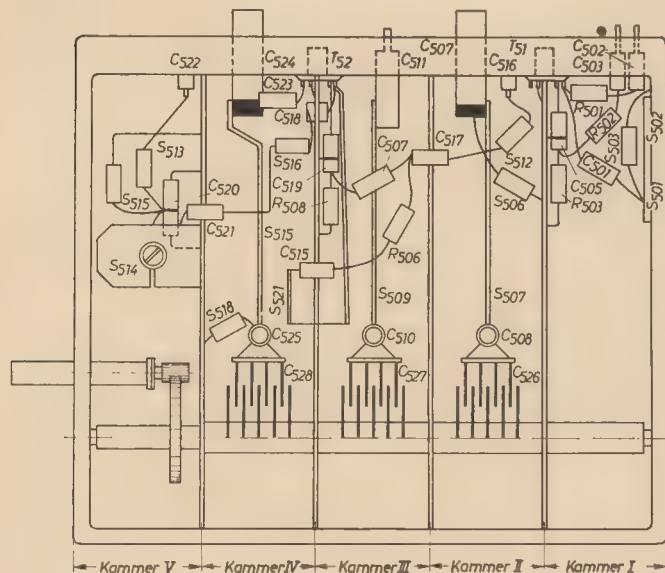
Lageplan und Abgleichpunkte des Philips-UHF-Tuners
